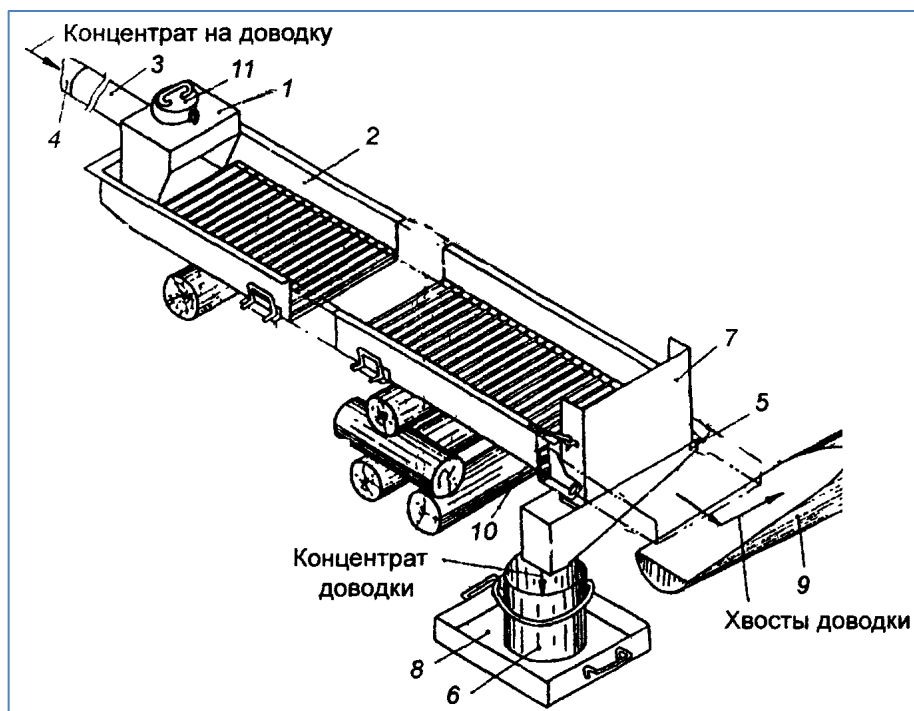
Доводочный шлюз ШД-1-580: 1 - питатель; 2 - шлюз; 3 - труба питателя; 4 - концентраторопровод; 5 - концентратный лоток; 6 - контейнер; 7 - поворотный лоток; 8 - подставка под контейнер; 9 - желоб для удаления хвостов доводки; 10 - крючок; 11 - крышка питателя
